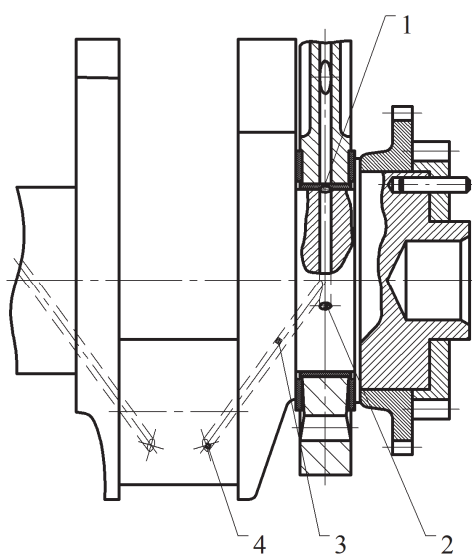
Схема подачи смазки к шатунным подшипникам коленчатого вала двигателей семейства КамАЗ: 1 – отверстие в коренном подшипнике; 2 – отверстие в коренной шейке; 3 – канал для подачи смазки в шатунный подшипник; 4 – отверстие в шатунной шейке
